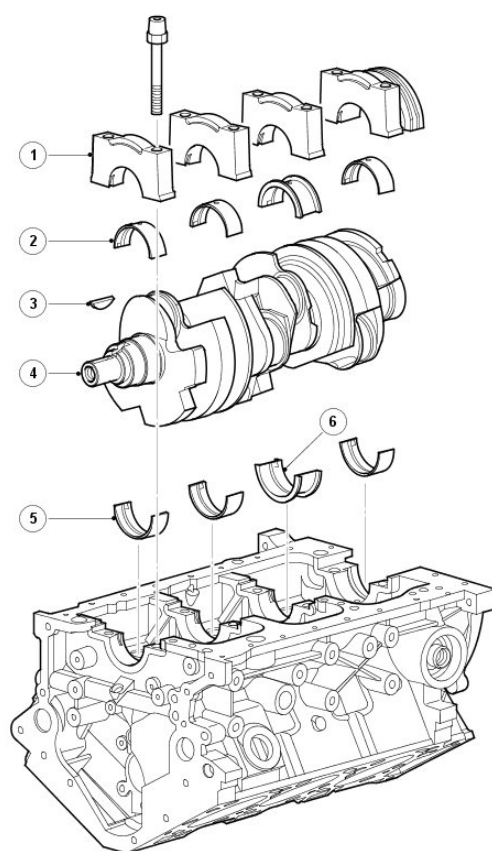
Коленчатый вал и коренные подшипники бензинового двигателя 4.0L V6
